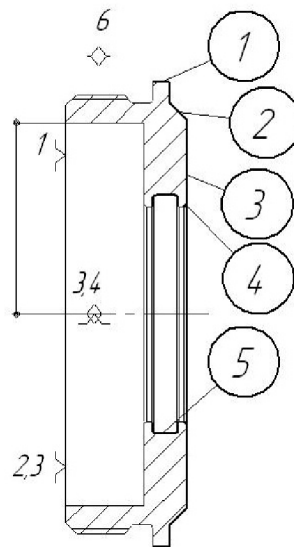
Схеми базування деталі на токарній обробці
